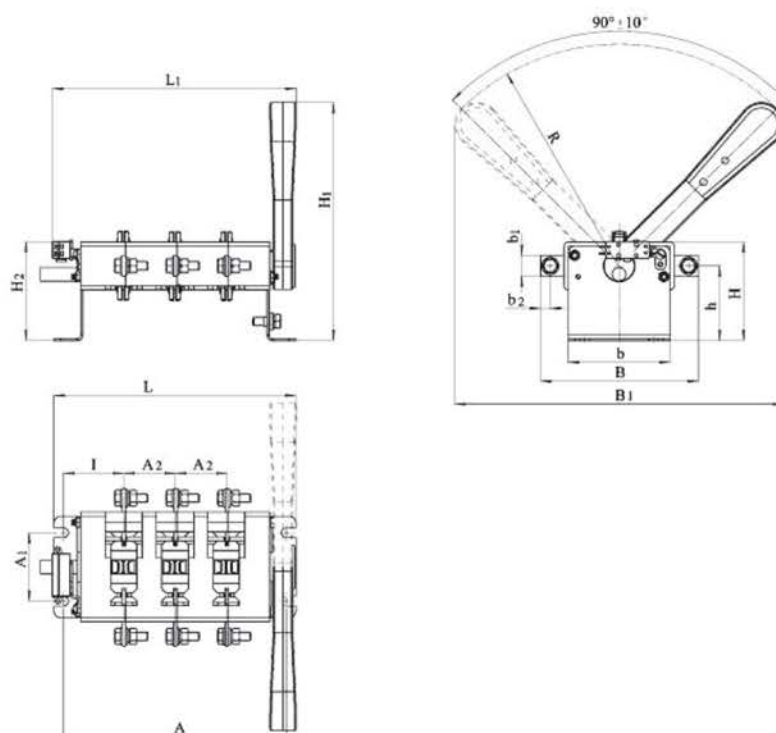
Выключатель-разъединитель трехполюсный на одно направление с передней смещенной рукояткой.
